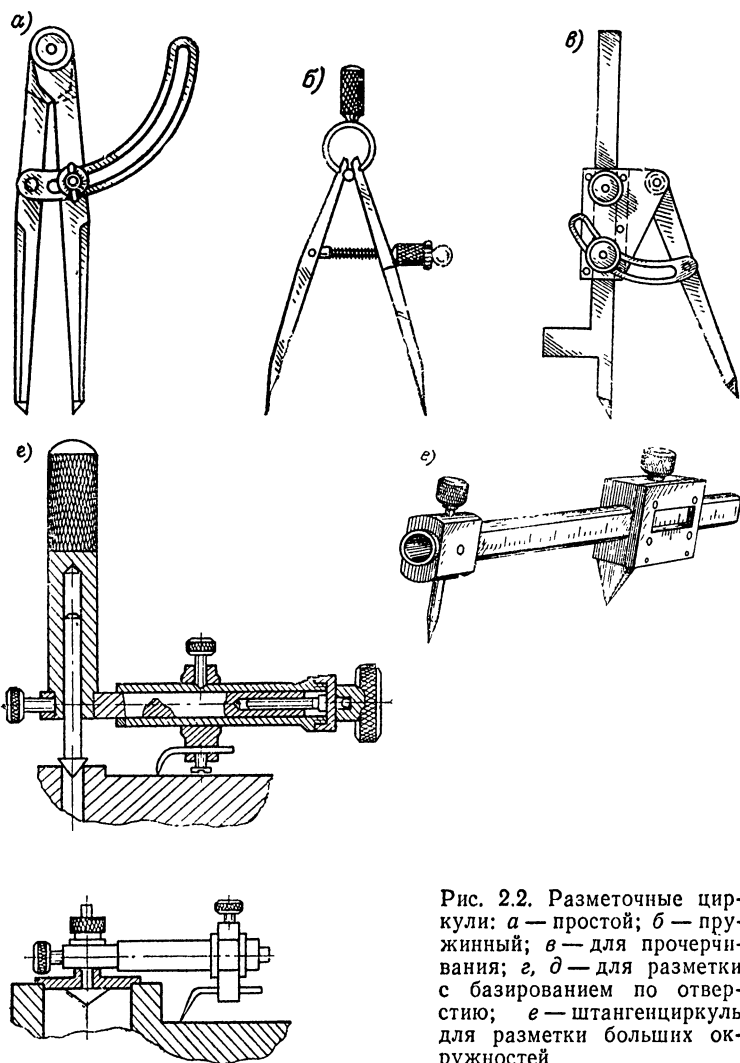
Разметочные циркули: а — простой; б — пружинный; в — для прочерчивания; г, д — для разметки с базированием по отверстию; е — штангенциркуль для разметки больших окружностей
